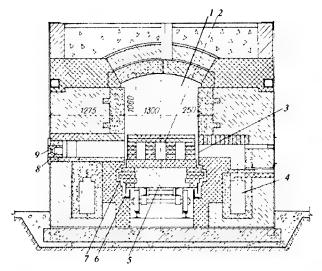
Печь периодического действия с выкатным подом: 1— рабочая камера; 2— выкатной под; 3— окно отбора дымовых газов; 4— сборные каналы; 5— вагонетка печи; 6— песочный затвор; 7— лабириннюе устройство; 8— тонка; 9— горелка
